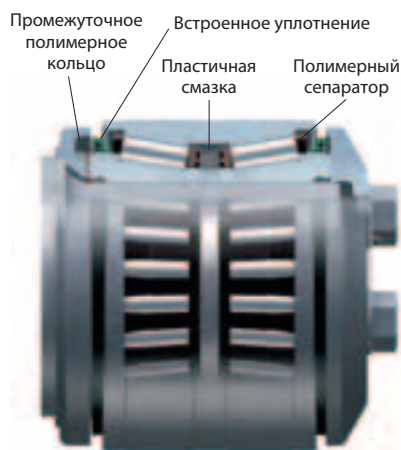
Основные компоненты конического роликового подшипника Compact TBU
